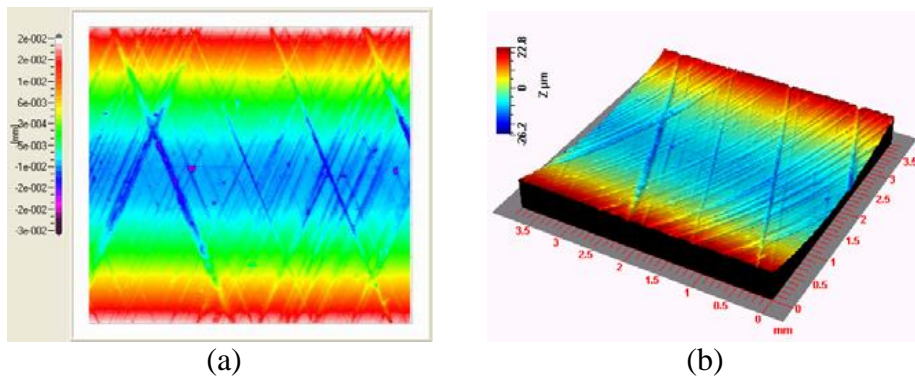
Surface de fût de carter cylindre (a) Vue 2D, (b) Vue 3D.
